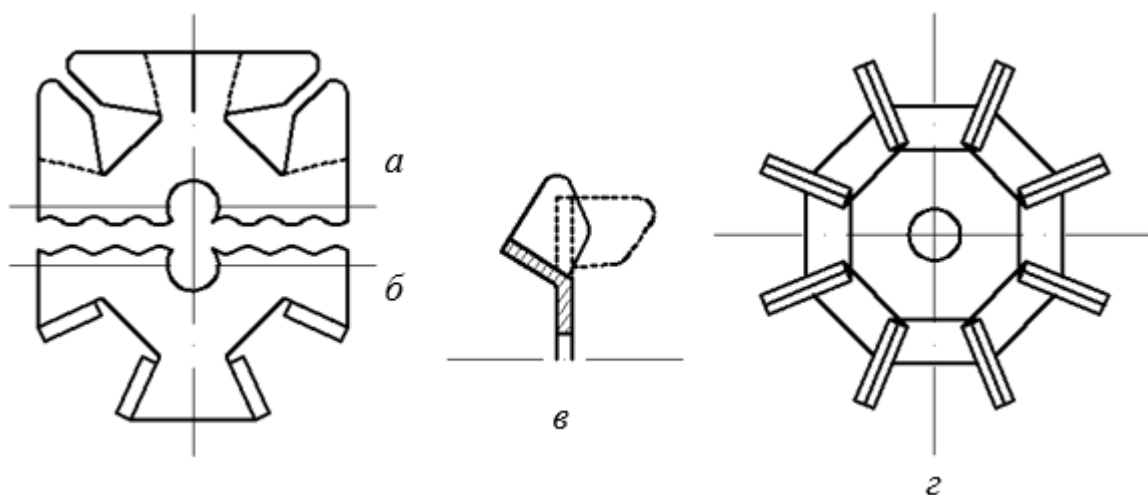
Спосіб виготовлення штампованого робочого колеса вентилятора зовнішнього обдуву статора: а – плоска заготовка; б – заготовка з вигнутими лопатями; в – формування модулів вигином ділянок плоскої заготовки між лопатями; г – робоче колесо вентилятора з двох накладених тангенціально зсунутих модулів.
